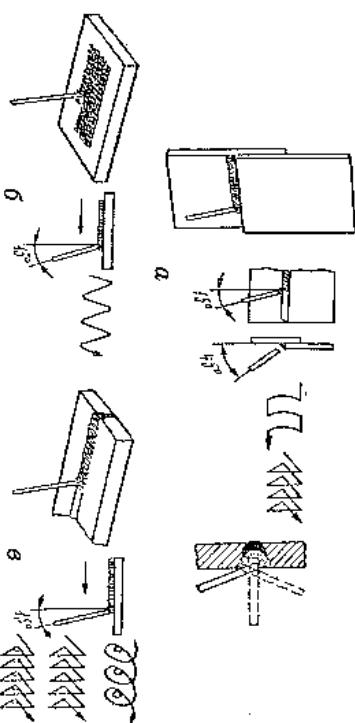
Положение и движение электрода при сварке в горизонтальном и потолочном положениях:
